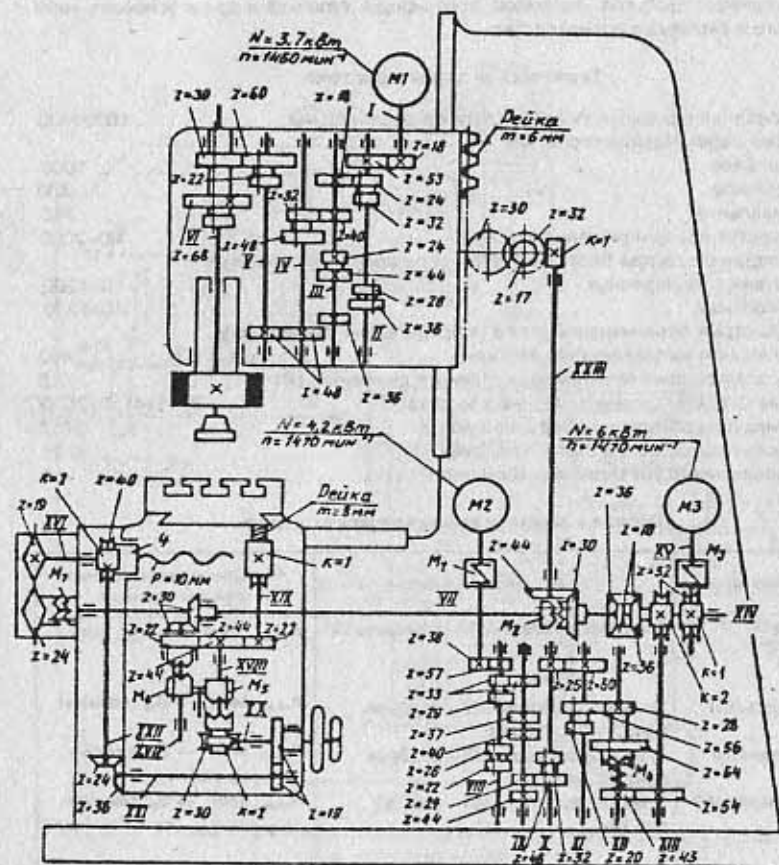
Кинематическая схема вертикально-фрезерного станка мод. 6A54
